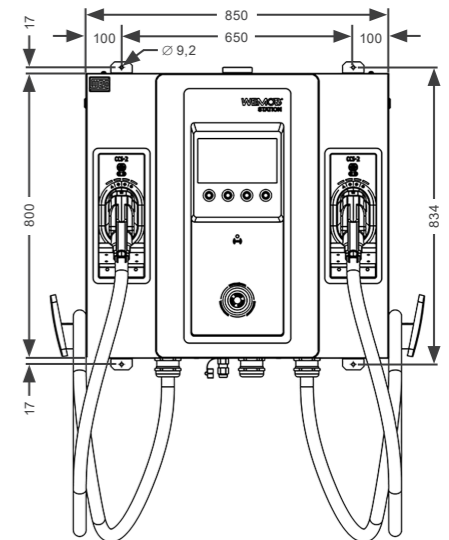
Dimensiones de la WEMOB-STATION (60/80 kW) para la fijación en la estructura de concreto - mm
